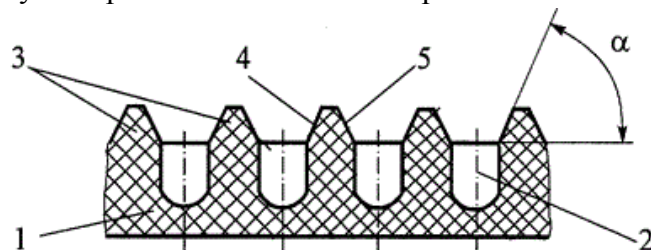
Разрез триерной поверхности: 1 - цилиндр; 2 – ячейки; 3 - реборды; 4, 5 – боковые поверхности
